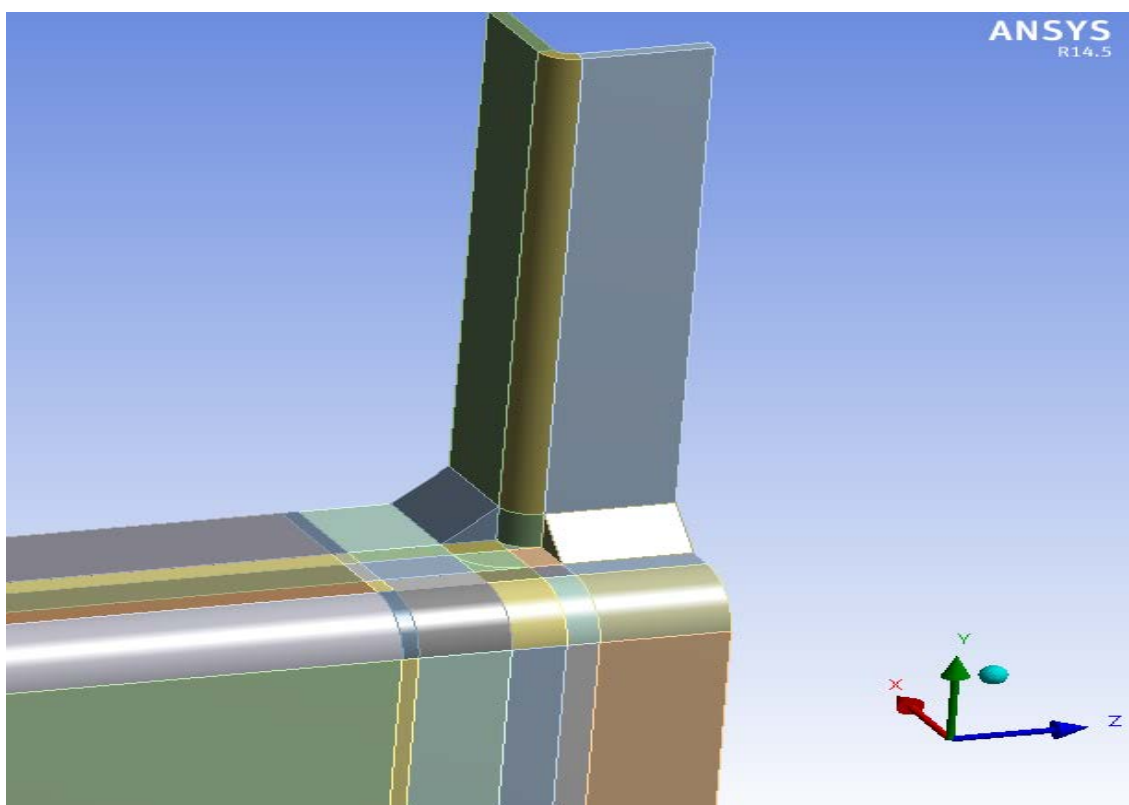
Modelo 2. Vista 3D de las soldaduras
